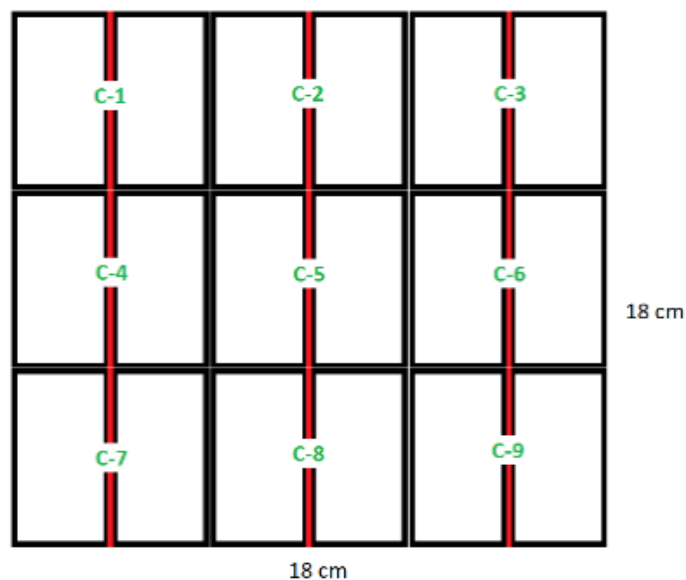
Divisão de uma chapa em 9 corpos de prova para soldadura.
